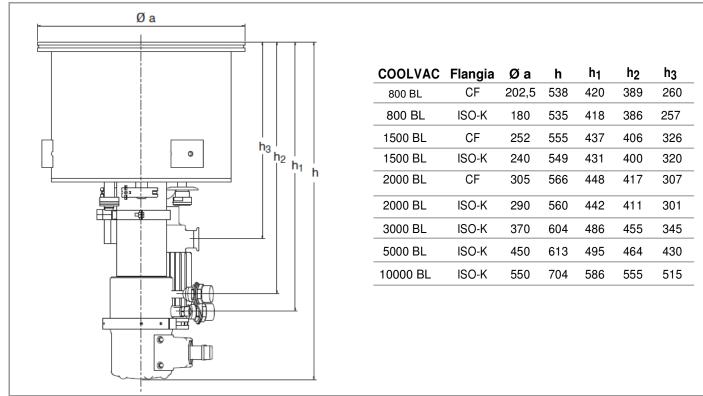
Disegno dimensionale della criopompa; dimensioni in mm
